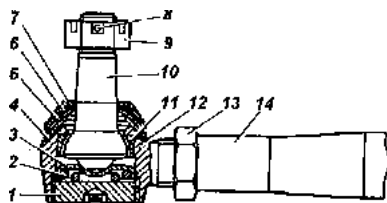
Шарнир рулевых тяг: 1 -заглушка; 2 -пружина; 3 -пята; 4 -шайба сферическая нижняя; 5 -шайба сферическая верхняя; 6 -кольцо защитное; 7 -пружинный колпачок; 8 -шплинт; 9,13 -гайка; 10 -палец шаровый; П -сухарь; 12 -наконечник; 14 -тяга
